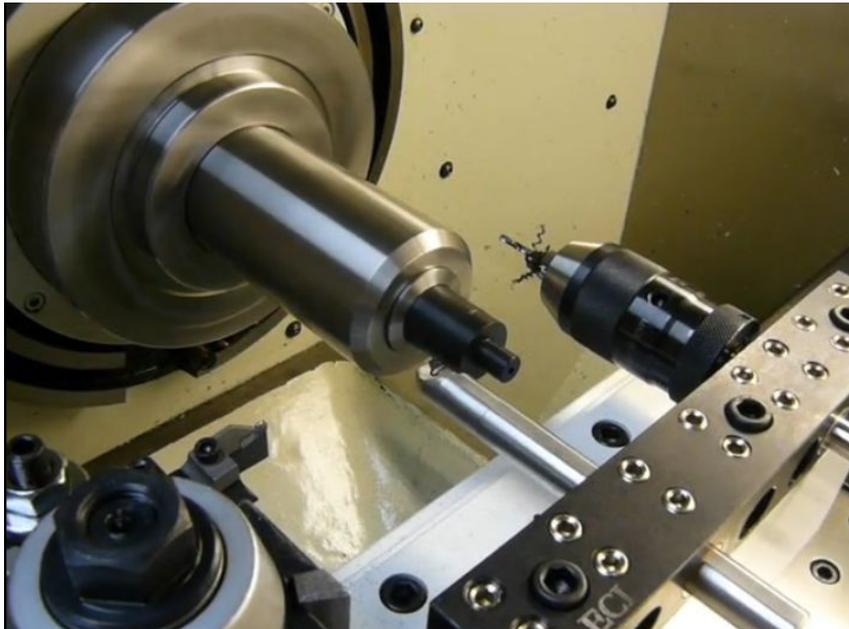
Linear Werkzeug (Gang Tool)
